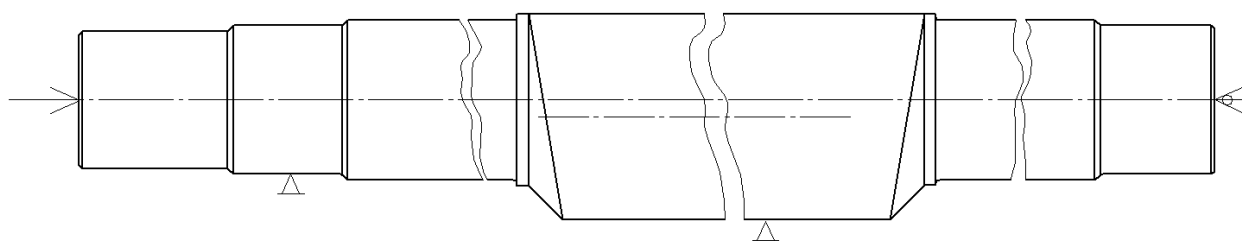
Схема базування вала при шліфувальній операції і токарній чистовій
